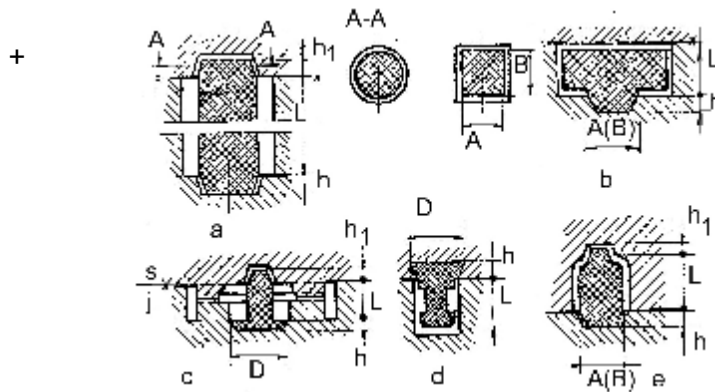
Construcția cutiilor de miez verticale și a mărcilor miezurilor verticale
